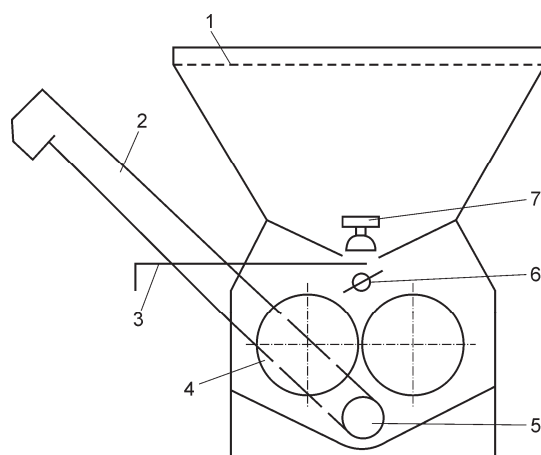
Конструктивная схема плющилки: 1 – решетка приемного бункера; 2 – выгрузной элеватор; 3 – заслонка; 4 – валцы; 5 – донный шнек; 6 – подающий ротор; 7 – магнитная защита
